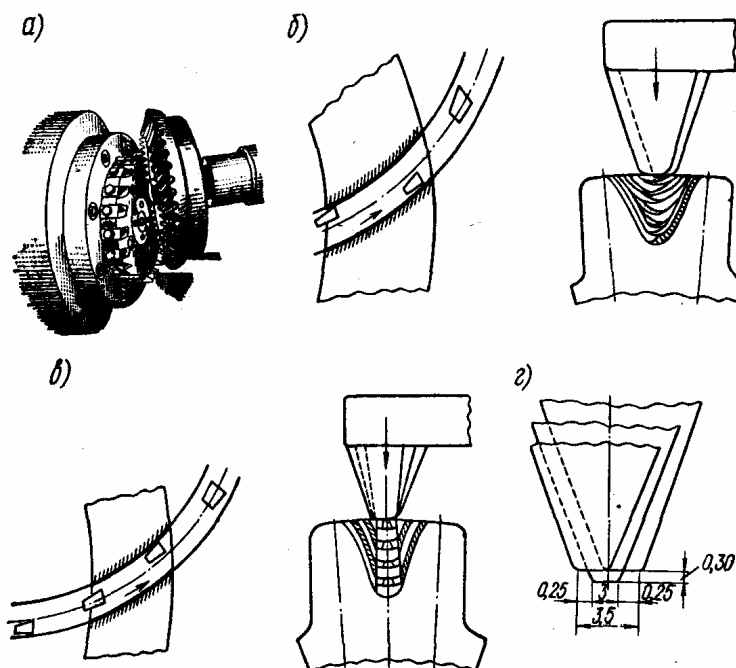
Нарезание конического зубчатого колеса с криволинейными зубьями:
